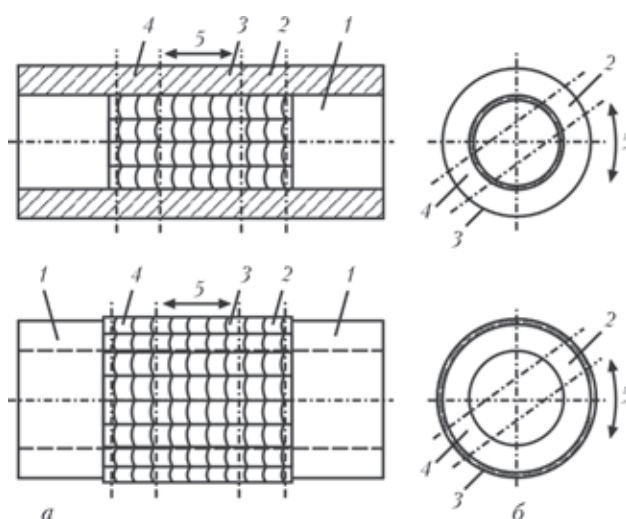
Порядок вырезки образцов из наплавленной трубы (контрольный образец): а — продольный наплавленный слой; б — кольцевой наплавленный слой (обозначения те же, что и на рис. 3)
